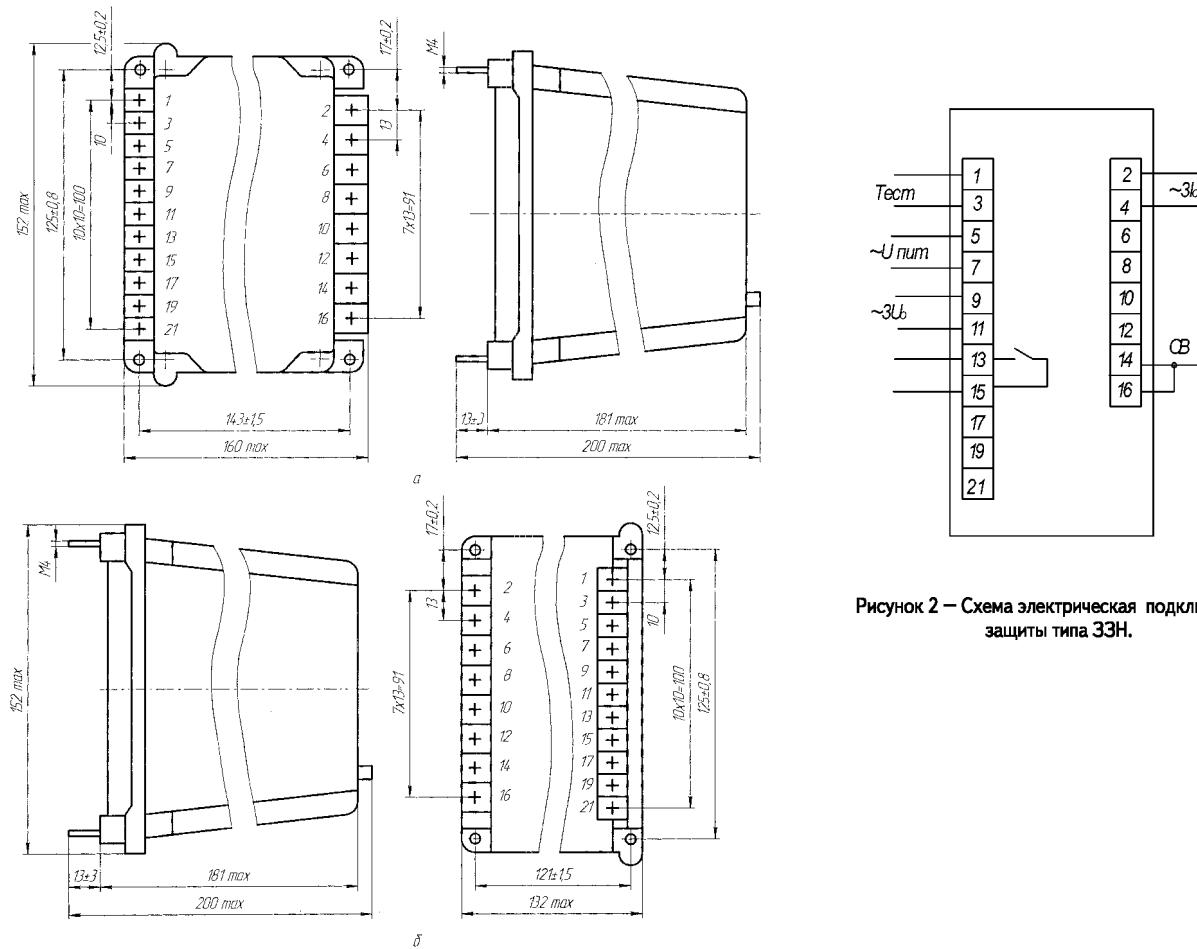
Габаритные, установочные и присоединительные размеры защиты типа ЗЗН.
